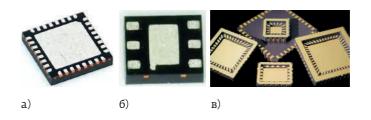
Основные типы безвыводных корпусов: a - QFN; б - DFN; в - LCC
